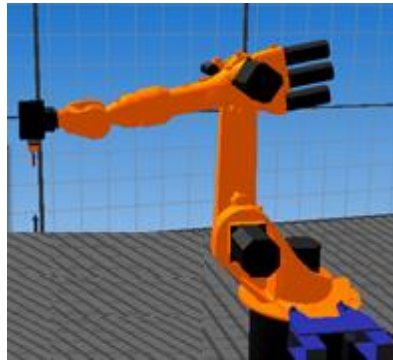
9: Robot KUKA KR16 con cabezal fresador adaptado en el KUKA Sim Pro.
